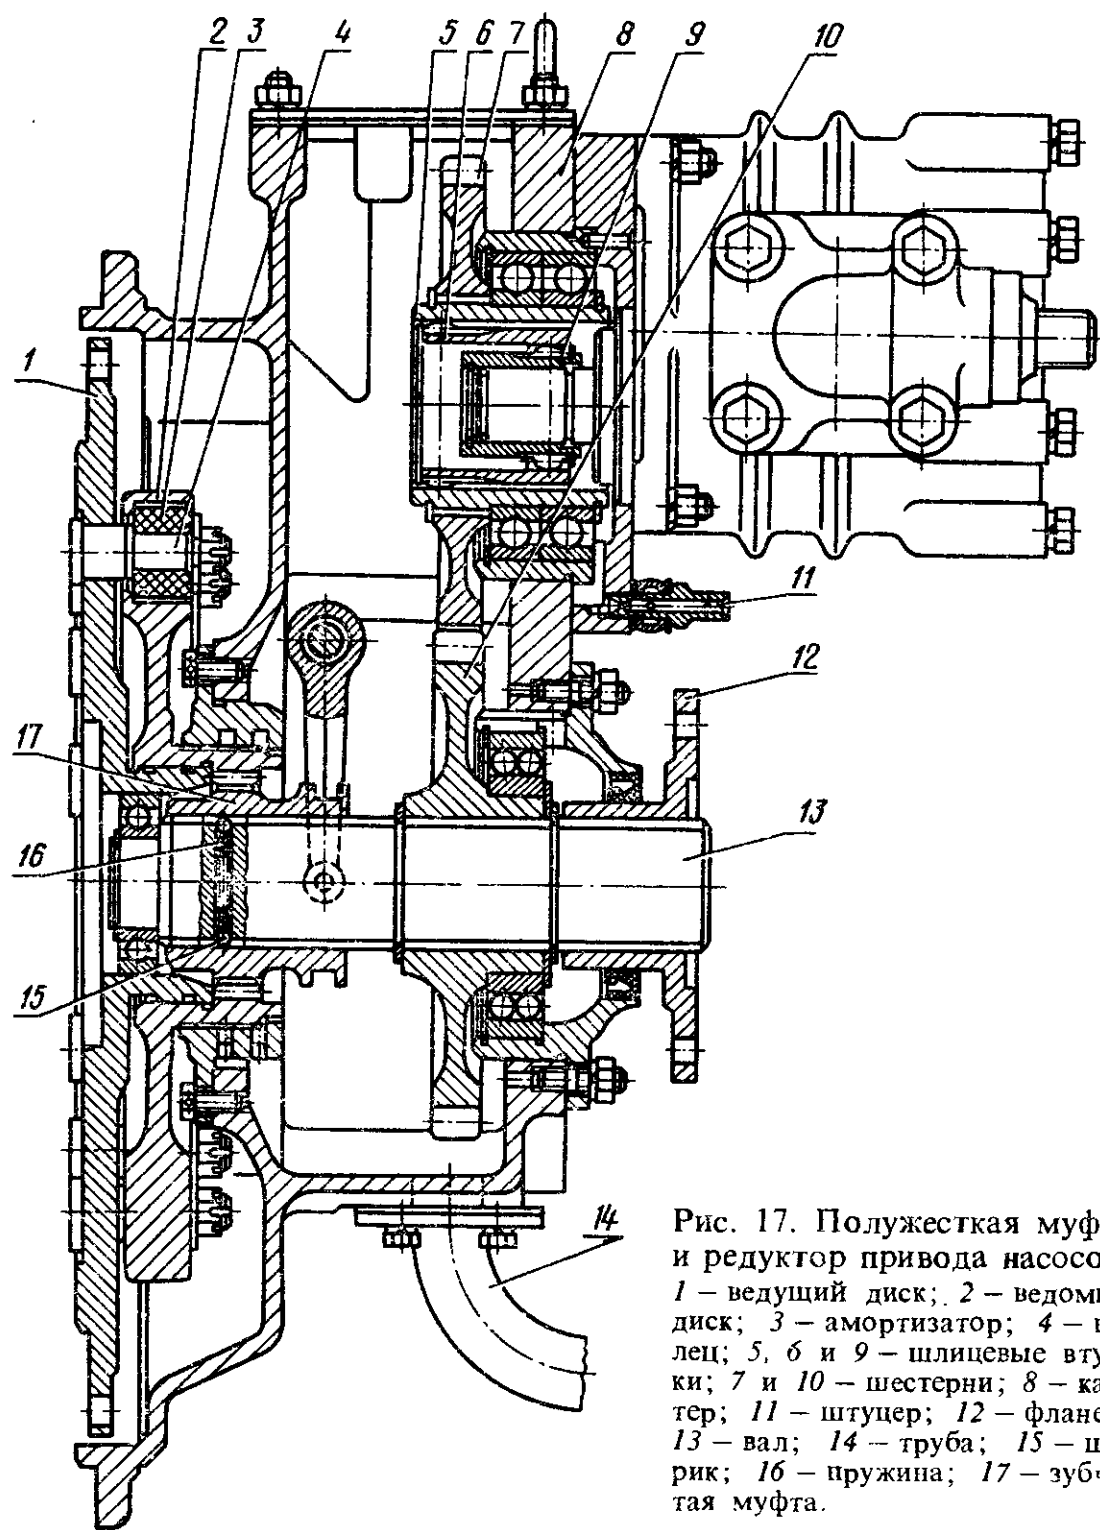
Полужесткая муфта и редуктор привода насосов: 1 — ведущий диск; 2 — ведомый диск; 3 — амортизатор; 4 — палец; 5, 6 и 9 — шлицевые втулки; 7 и 10 — шестерни; 8 — картер; 11 — штуцер; 12 — фланец; 13 — вал; 14 — труба; 15 — шарик; 16 — пружина; 17 — зубчатая муфта.
